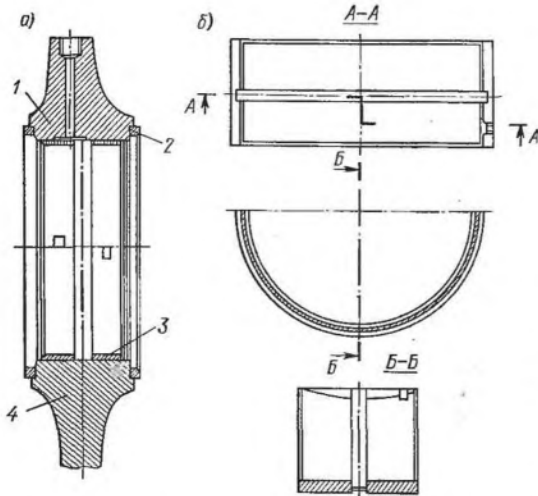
Конструкция опорного подшипника с тонкостенным вкладышем: а — корпус подшипника; б — вкладыш;
